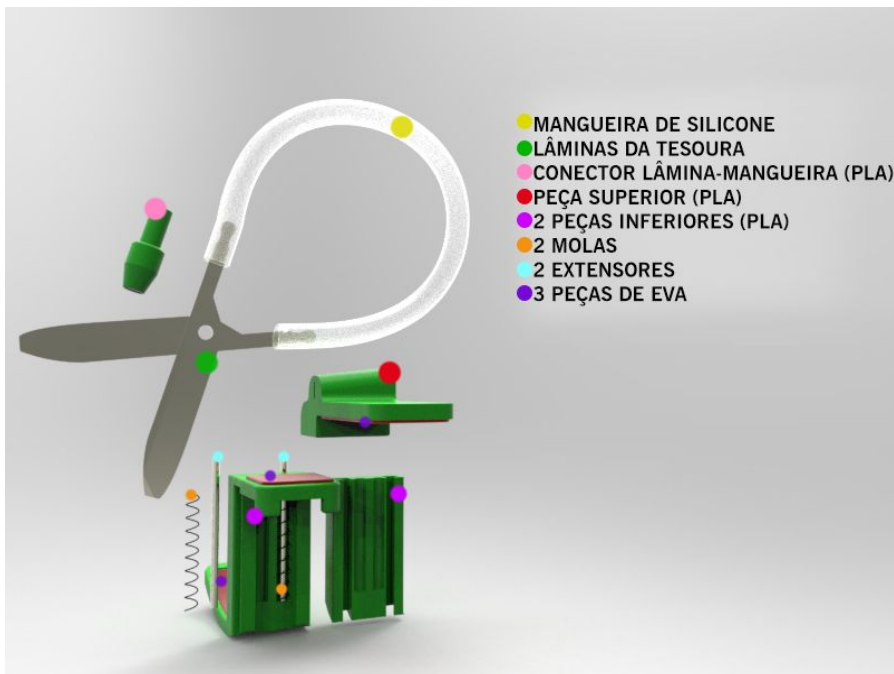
Vista explodida da tesoura mola com suporte para mesa. Fonte: Autora 2019.
